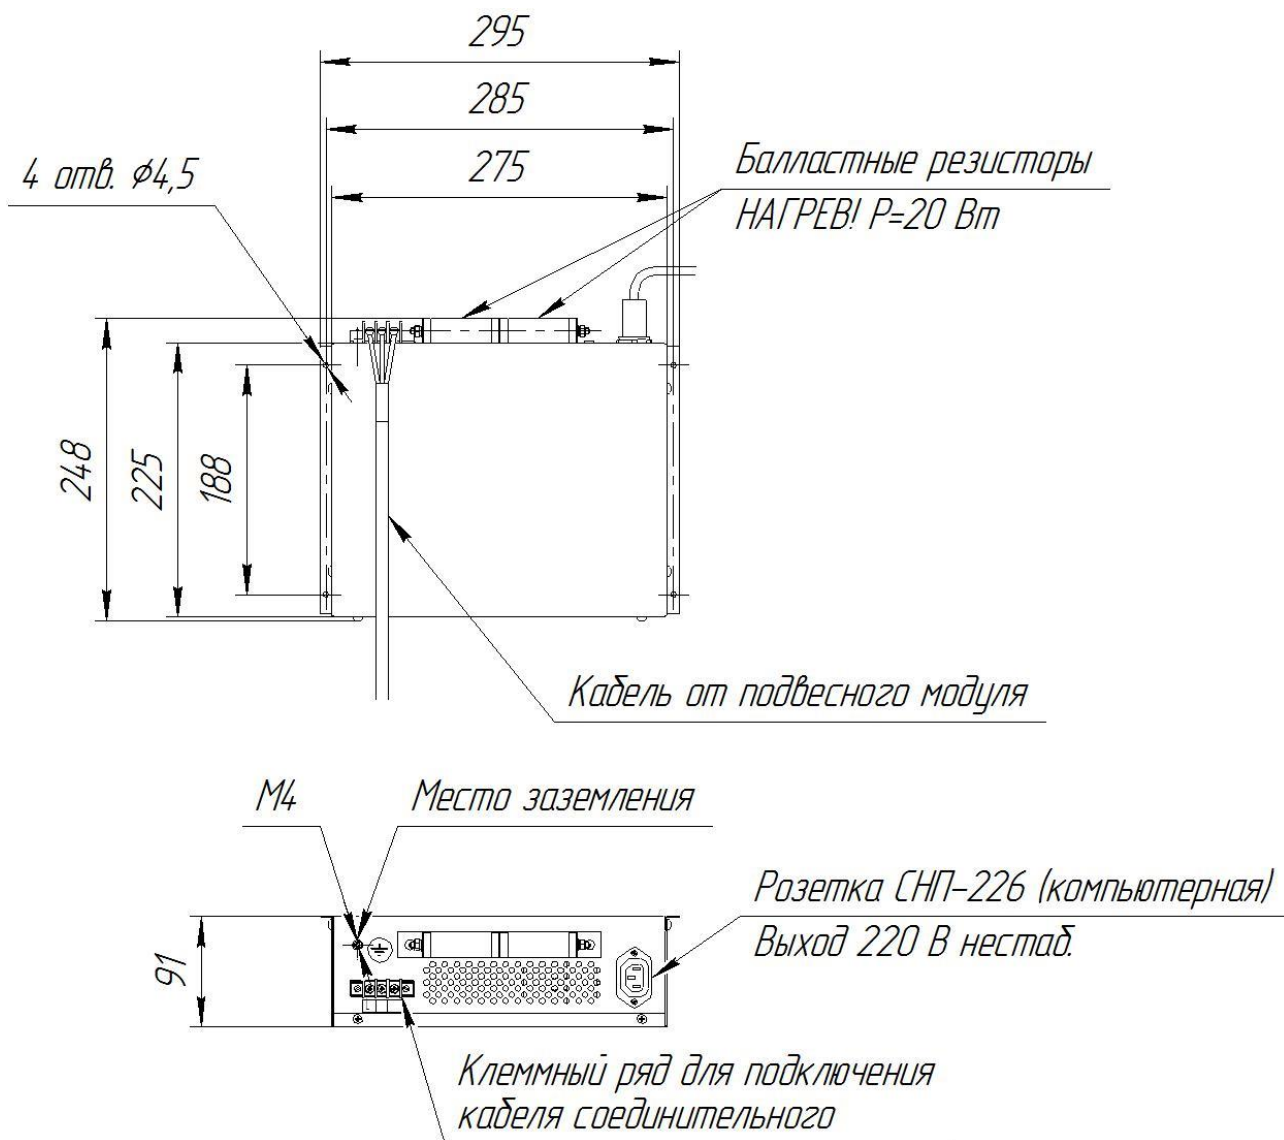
Общий вид и габаритные размеры модуля сопряжения
